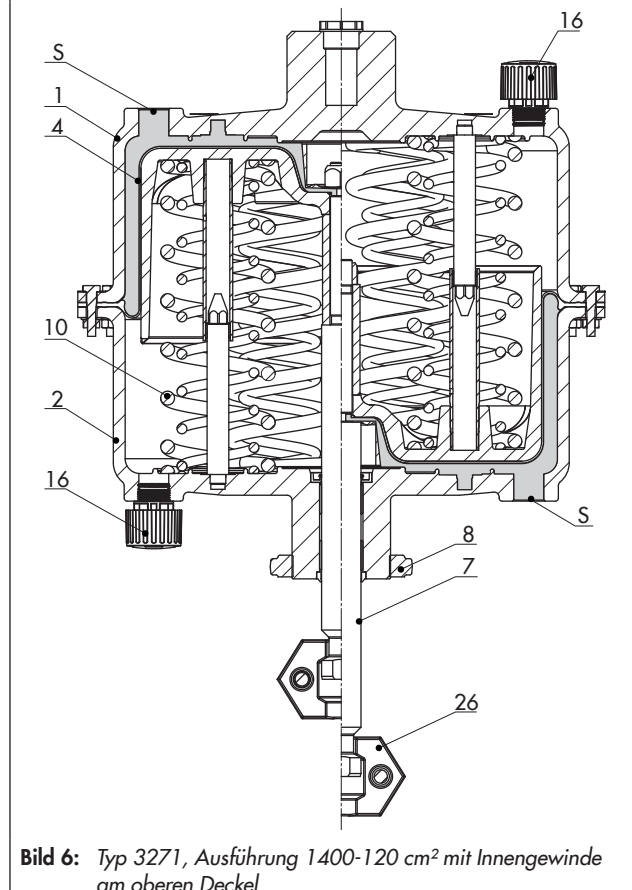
Typ 3271, Ausführung 1400-120 cm^2 mit Innengewinde am oberen Deckel
